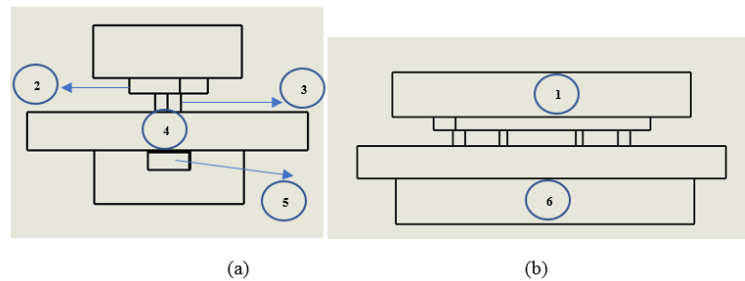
(a) Vista frontal del molde; (b) Vista Lateral del molde
